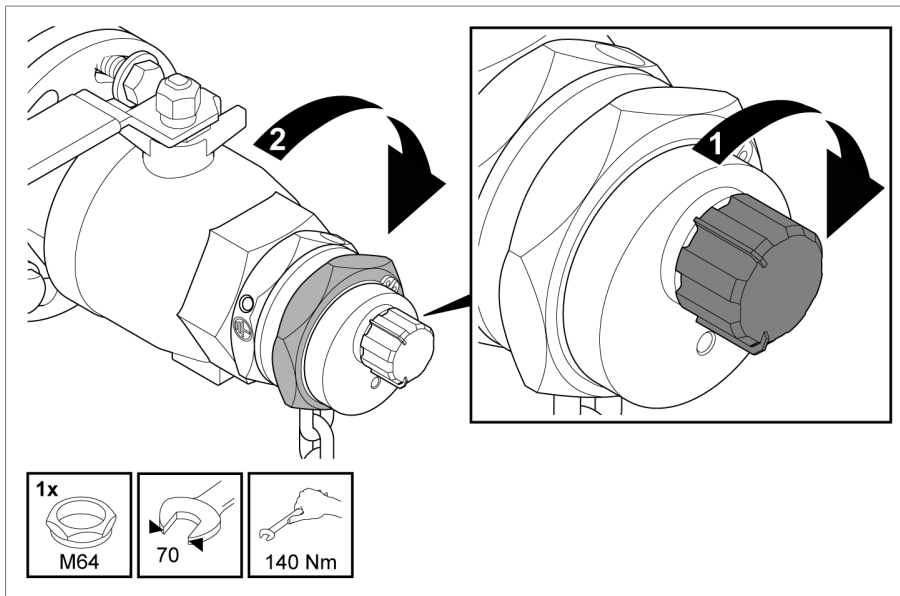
Serrare il raccordo filettato di bloccaggio della valvola a sfera
